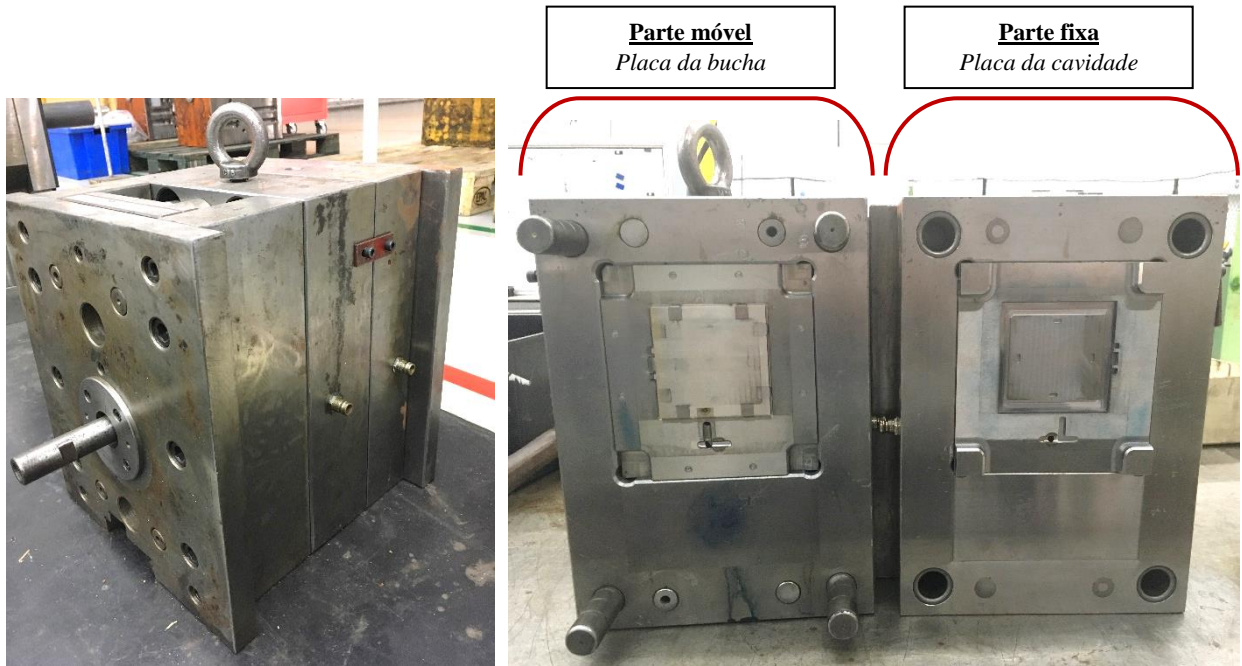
Molde (parte móvel e parte fixa) da frame a desenvolver
